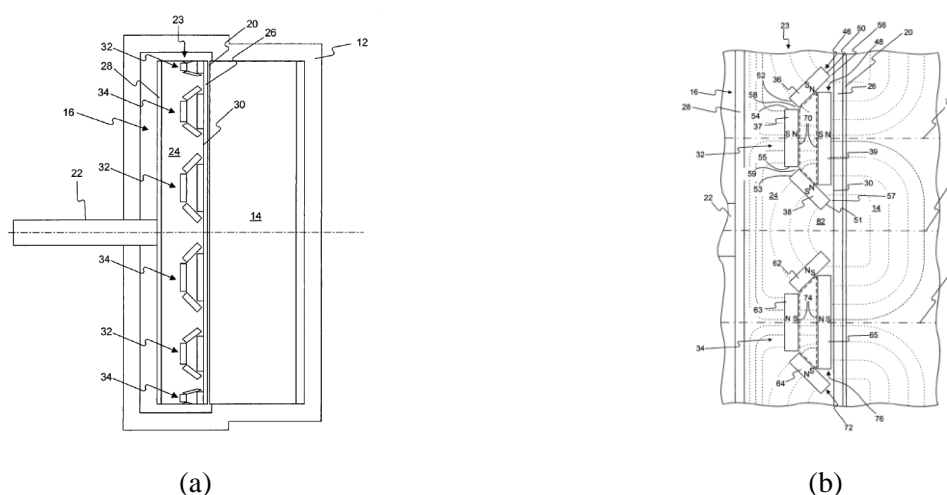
IPM à flux axial TORUS : (a) section de la machine et vue du rotor, et (b) circulation du flux dans la machine [55].
